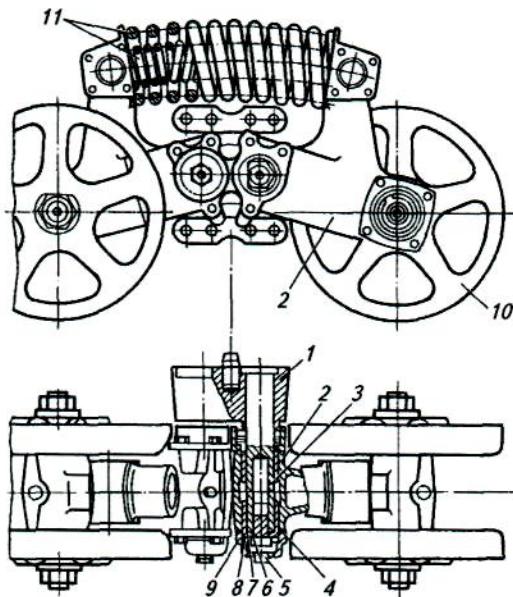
Каретка подвески трактора ХТЗ-150-09
